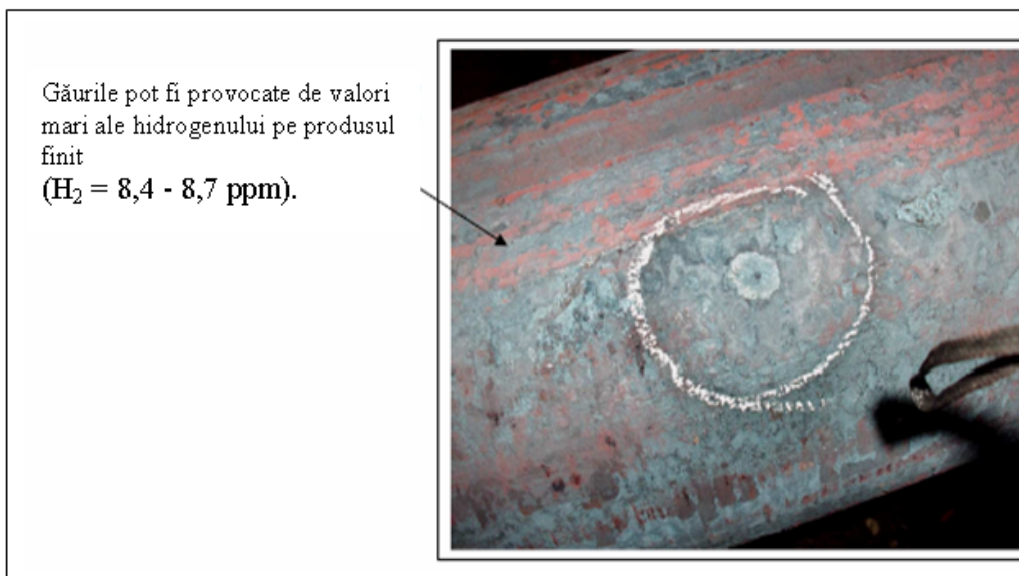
Defect tip gaură – țagă Φ 270mm
